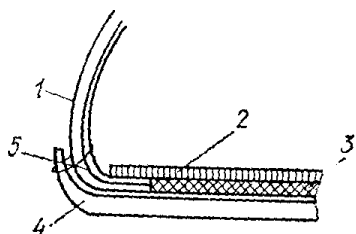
Бортовой метод: 1 – заготовка; 2 – основная стелька; 3 – простилка;
